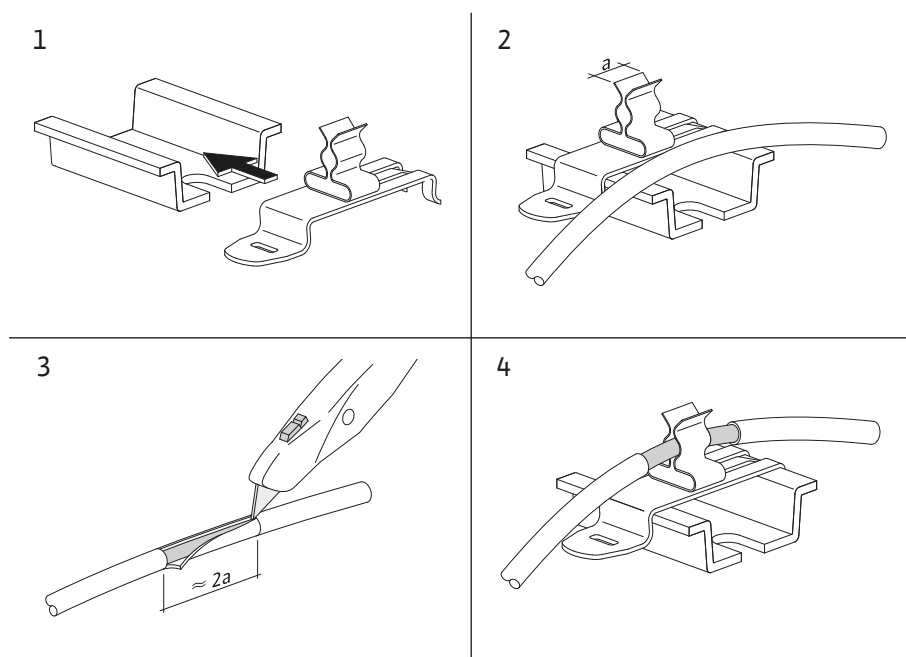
Pålegging av kabelisoleringer på jordingsskinnen
